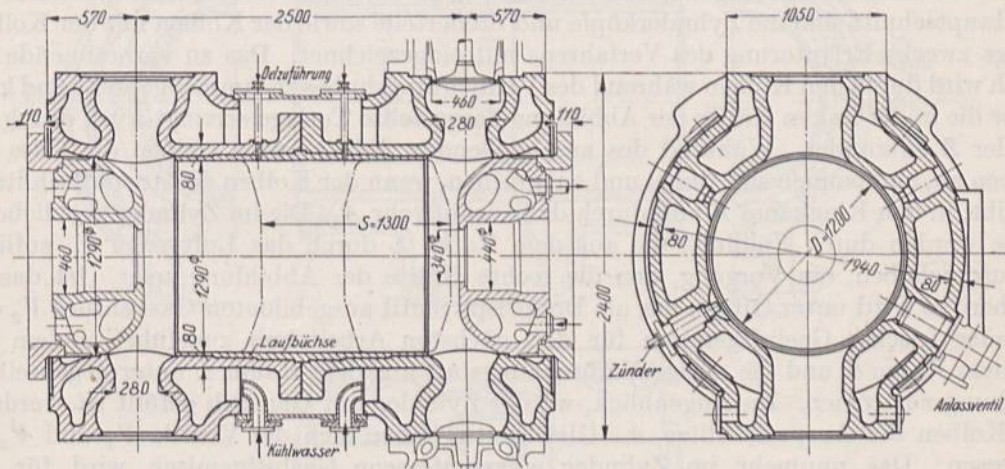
Großgasmaschinenzylinder von Ehrhardt und Sehmer. M. 1:50.
